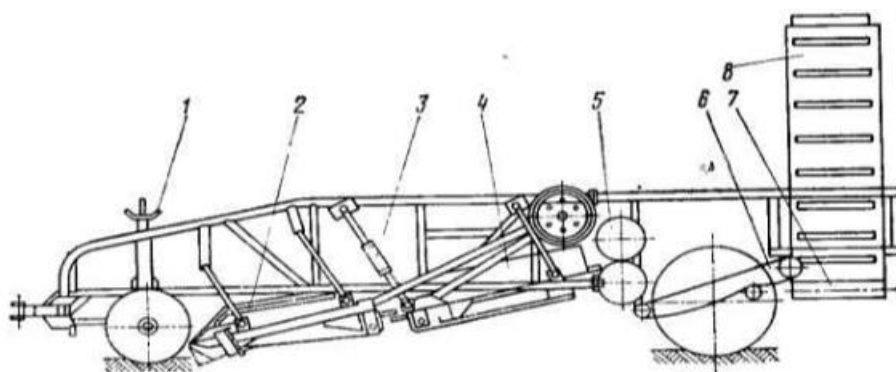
Схема цибулезбиральної машини ЛКГ-1,4: 1 – гвинтовий механізм регулювання глибини підкопування; 2 - переднє решето грохоту; 3 – регульована підвіска; 4 - заднє решето грохоту; 5 - комкодавильні балони; 6 – поздовжній елеватор; 7 – поперечний елеватор; 8 - завантажувальний транспортер [5].
